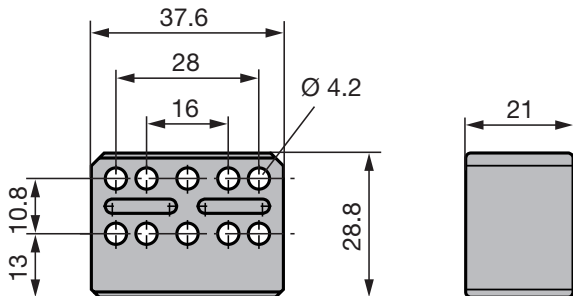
Einbaumaße Positionsgeber BTL6-A-3800-2
